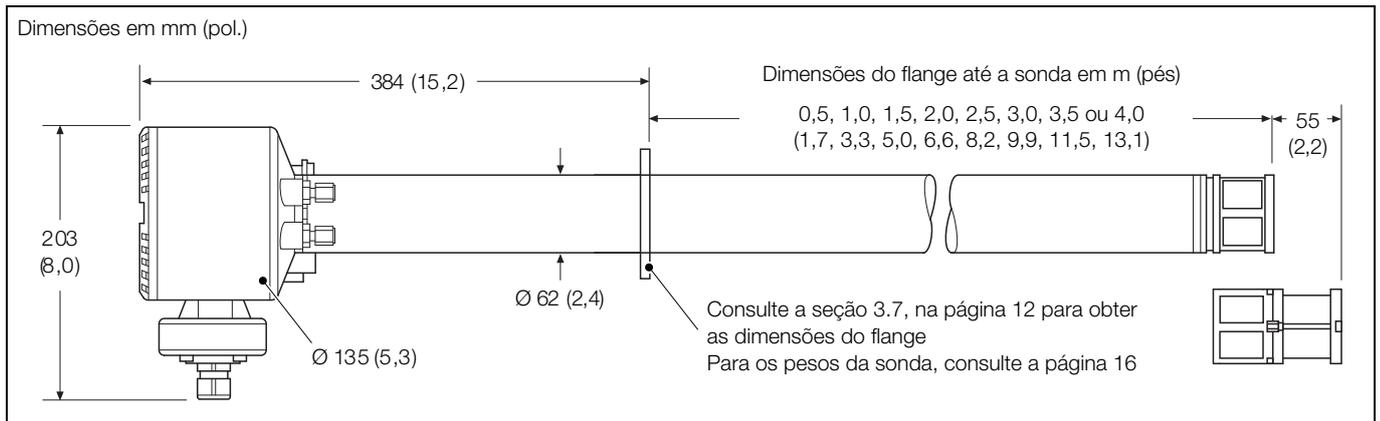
Dimensões gerais – sonda remota Endura AZ20
